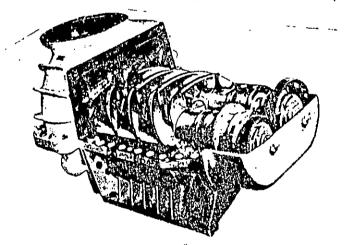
Un compresor de tornillo rotatorio seco.
